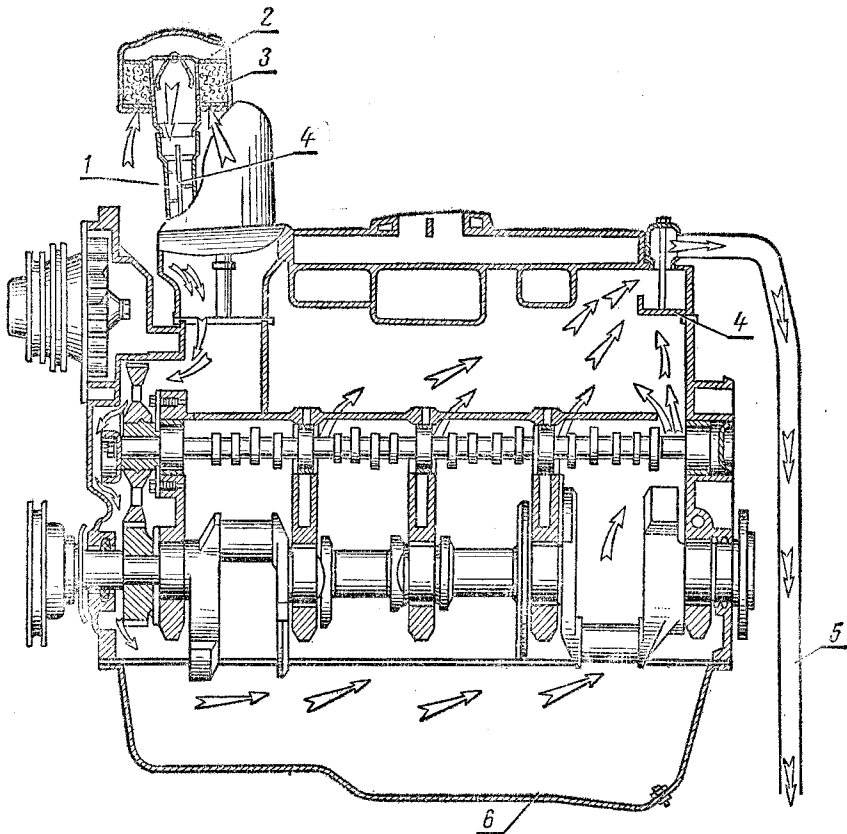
Схема вентиляции картера двигателя ГАЗ-53:
